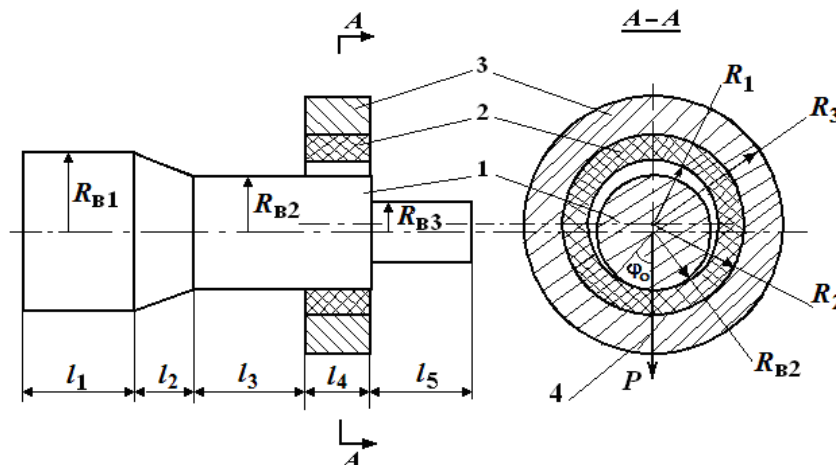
Схема подшипника скольжения: 1 – вал, 2 – полимерная втулка, 3 – обойма, 4 – ось нагружения подшипника, P – нагрузка поджатия
